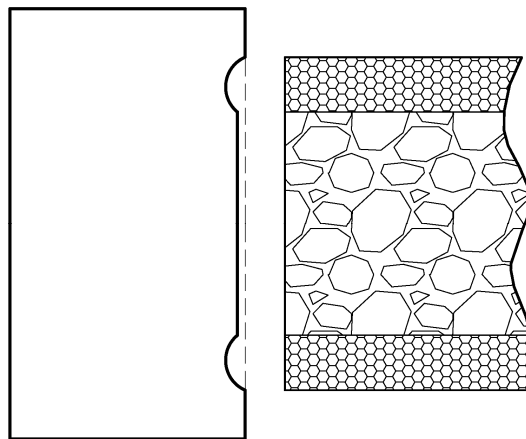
Схема износа резца при фрезеровании ламинированных ДСтП
